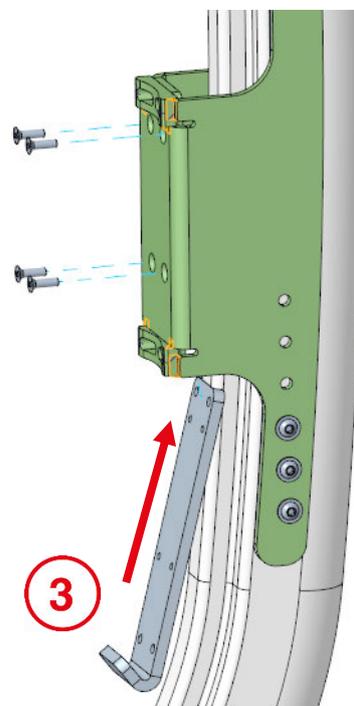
Montage Gewindeplatte; Außenansicht;
